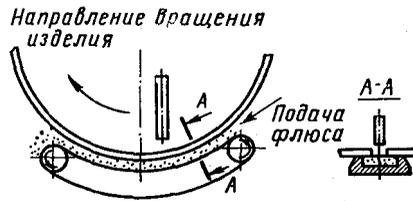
Схема флюсоремной подушки для сварки кольцевых швов
